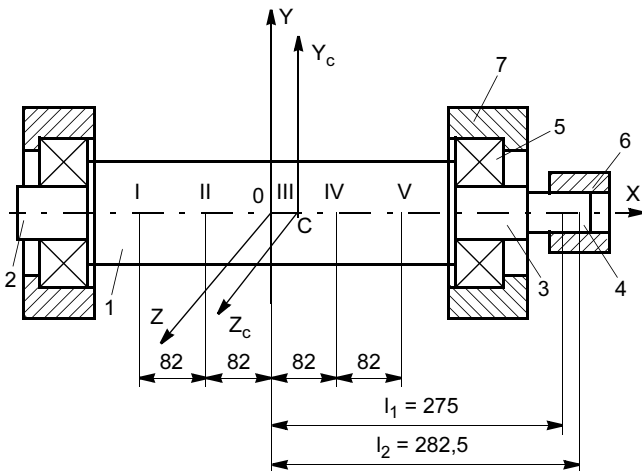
Схема сборки составной конструкции: I—V — положения диска
